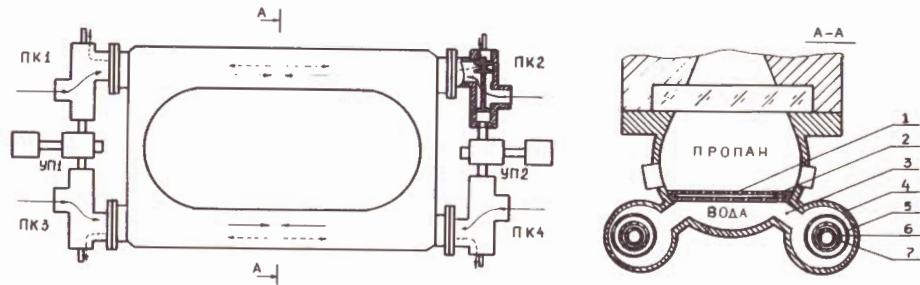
Схема механизма расширения: 1 - плоская мембрана, 2 - плоская решетка; 3 - патрубок; 4 - корпус расширительного устройства; 5,6 - цилиндрическая мембрана; 7 - цилиндрическая решетка.
